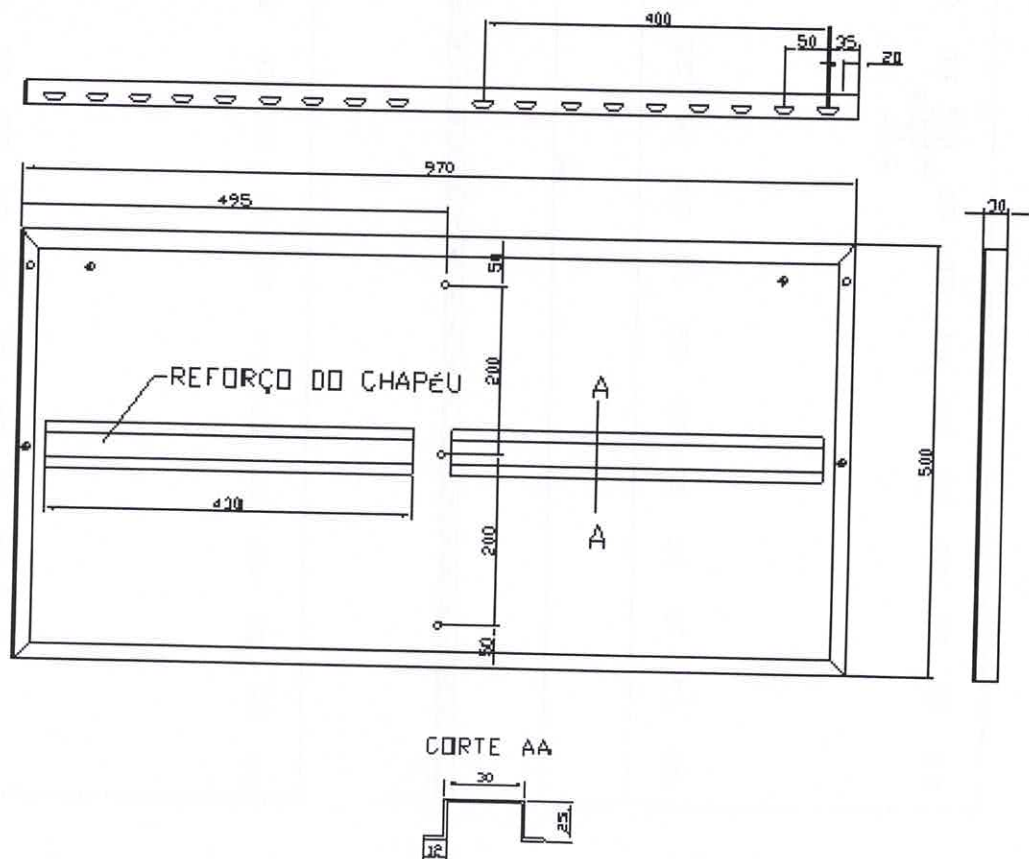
Detalhe do chapéu com seu reforço (mm)
